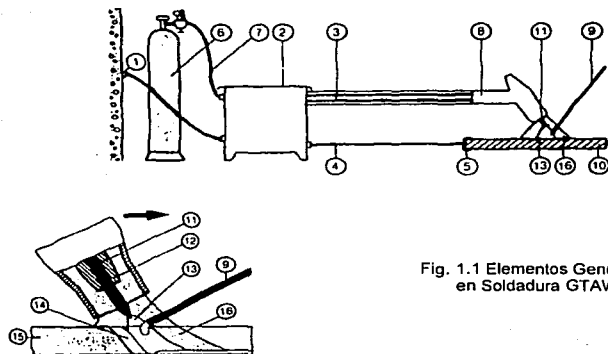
Elementos Generales en Soldadura GTAW
